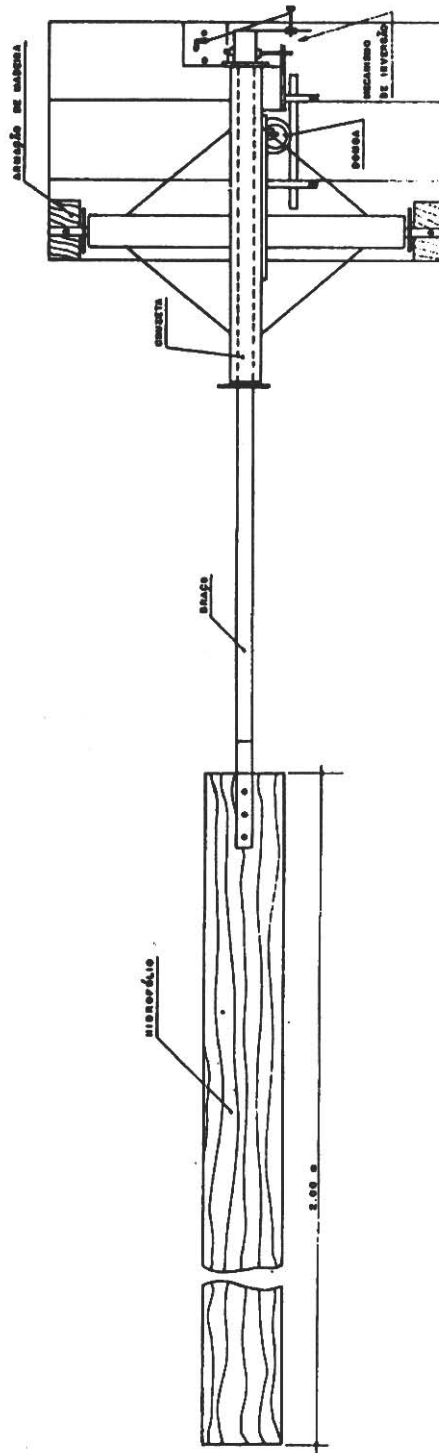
PLANTA BAIXA DA ARMAÇÃO DE MADEIRA
